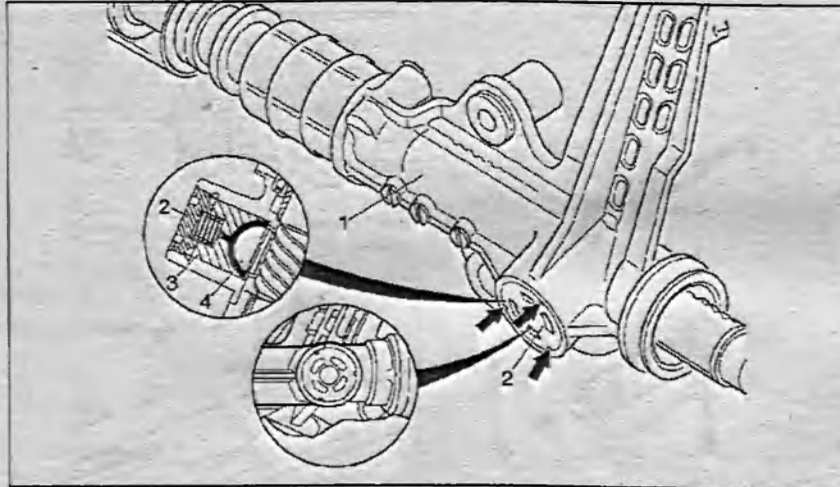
Регулировка зазора между рейкой и шестерней рулевого механизма:
